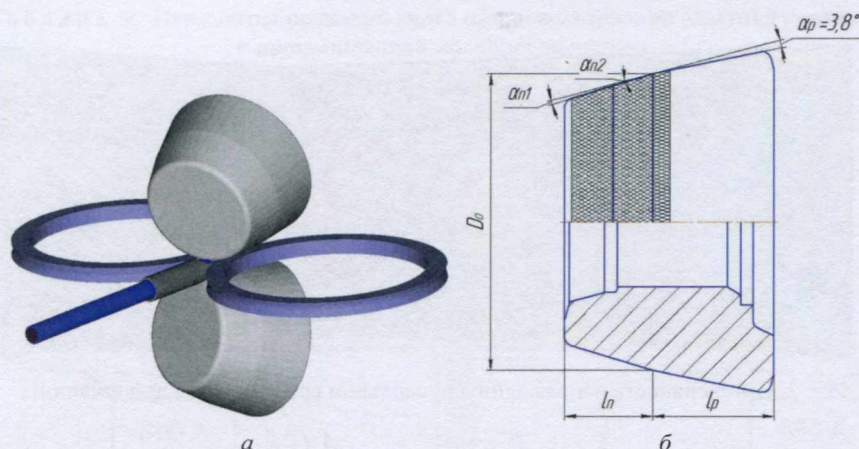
Геометрическая модель процесса прошивки (а) и профиль грибовидного вала (б)
